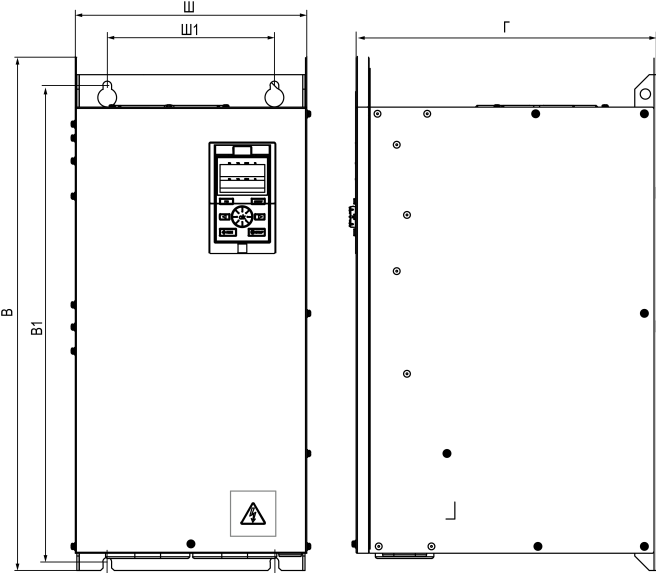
Габаритные размеры прибора в корпусе типоразмера 6
